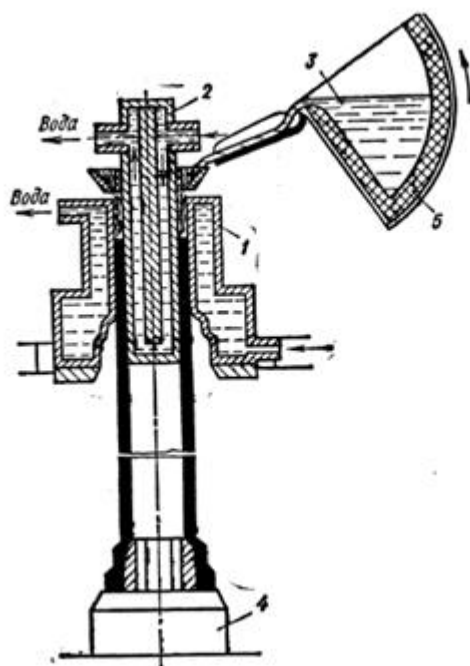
Схема вертикальной установки для полунепрерывного литья: 1 – кристаллизатор (литейная форма); 2 – пустотелый (охлаждаемый водой) стержень; 3 – жидкий сплав; 4 – ложное дно-затравка; 5 – ковш.
